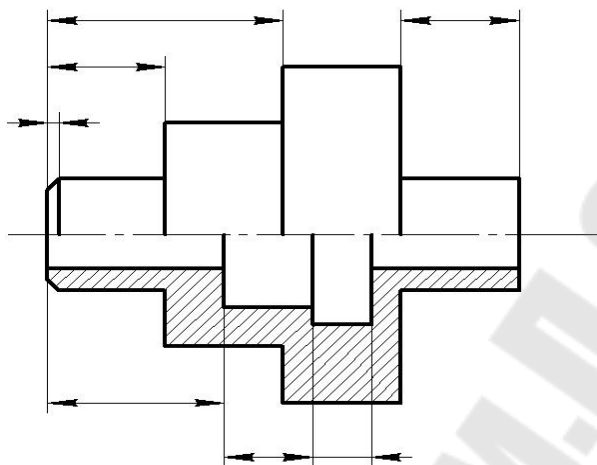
Группирование размеров внутренних и внешних очертаний детали
